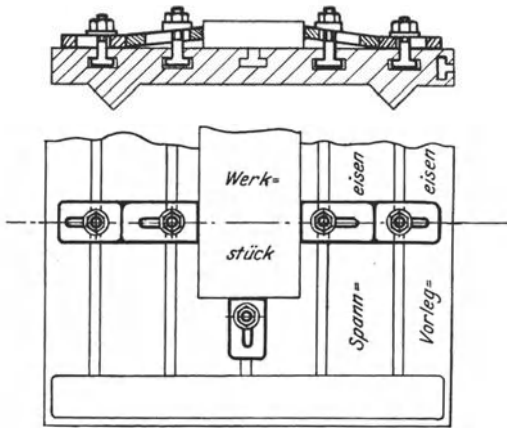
Eine ältere Aufspannart für Hobelmaschinen.
